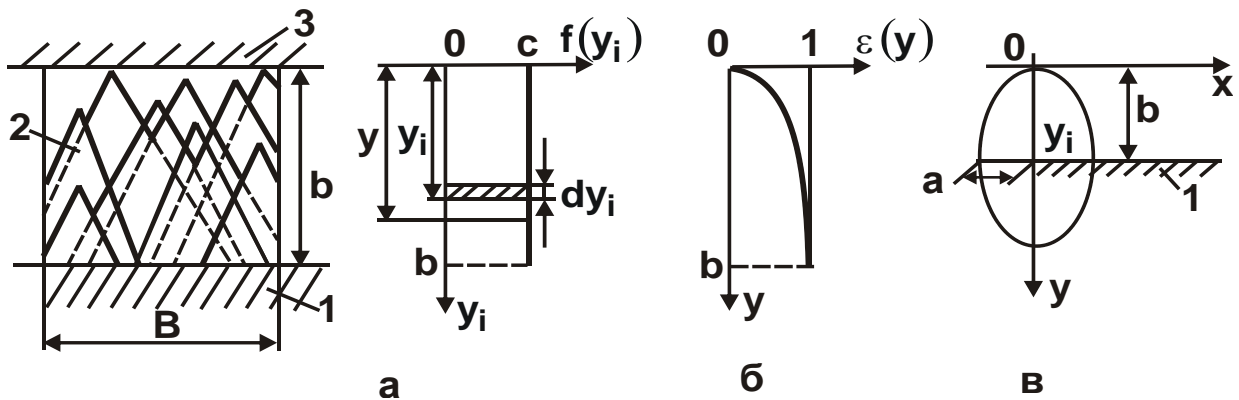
Розрахункова схема статичної моделі робочої поверхні круга: 1 – зв'язка круга; 2 – зерна круга; 3 – матеріал оброблюваного виробу
